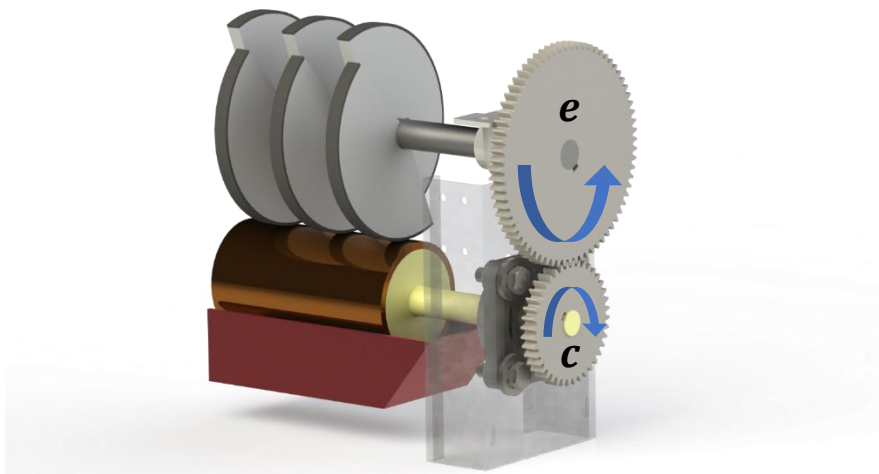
Sistema de engranajes encolador cilindro recolector
